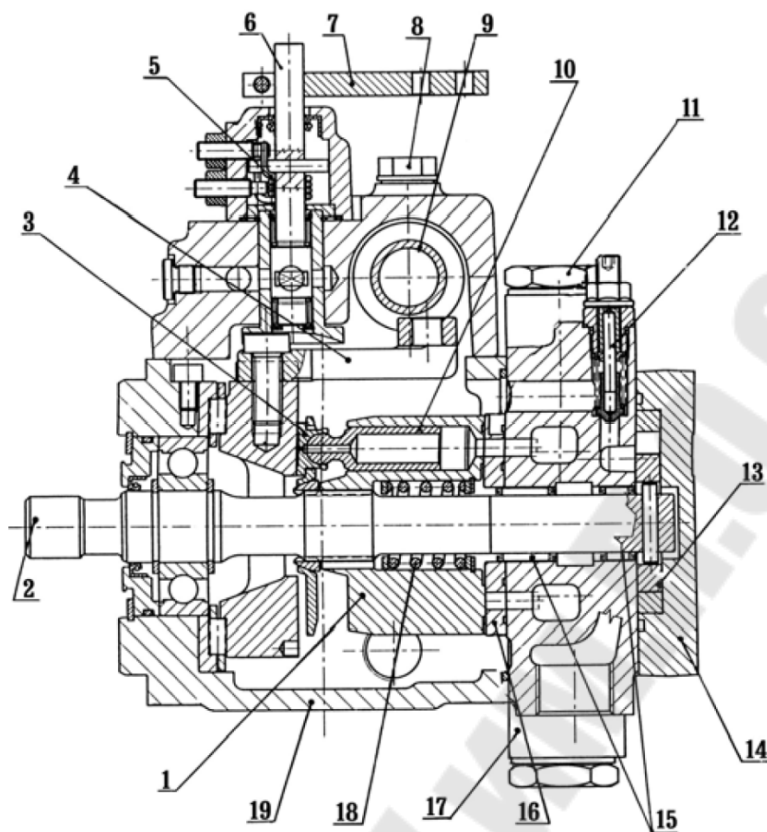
Насос аксиально-поршневой типа V250: 1 – блок цилиндров; 2 – приводной вал; 3 – гидростатический подпятник; 4 – рычаг поворота наклонного диска; 5 – возвратная пружина; 6 – ось валика механизма наклона шайбы; 7 – рукоятка механического управления подачей; 8 – заглушка в отверстии для подвода РЖ к цилиндру сервоуправления подачей; 9 – цилиндр сервоуправления; 10 – поршень; 11 – заглушка в отверстии отвода (подвода) основного потока; 12 – переливной клапан насоса подпитки; 13 – шестеренный насос; 14 – крышка шестеренного насоса; 15 – роликоподшипники приводного вала; 16 – распределительный диск; 17 – задняя крышка; 18 – винтовая пружина; 19 – корпус насоса.
